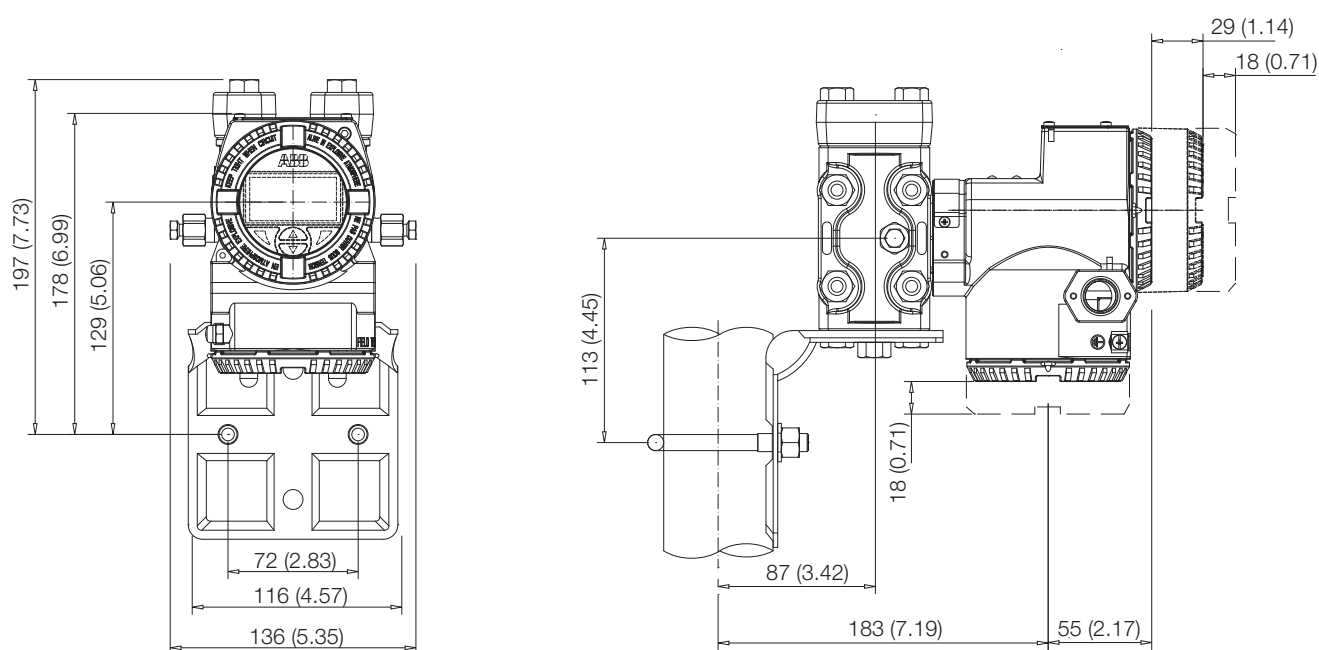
Преобразователь дифференциального давления с корпусом DIN, установленный на вертикальной трубе с помощью опционного монтажного кронштейна (B2), установка для измерения ВОЗДУХА/ГАЗА
